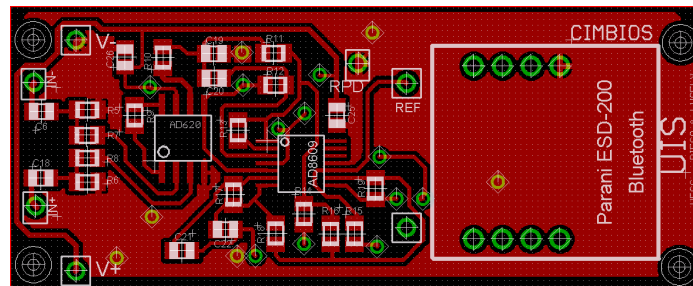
Carpa superior del PCB, etapa de adquisición de la Señal
